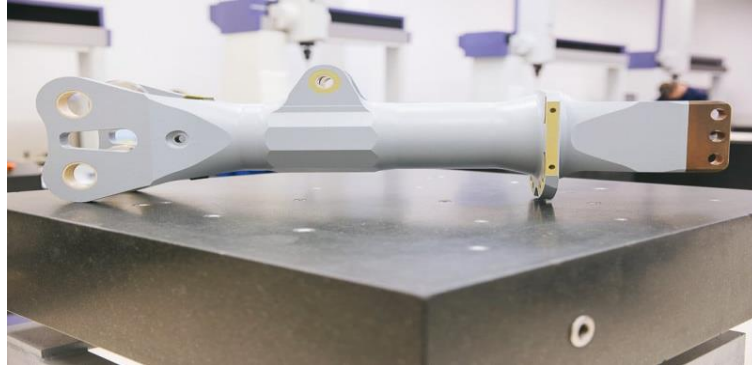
Punho do Rotor do EC 725 Fabricado no Brasil.
